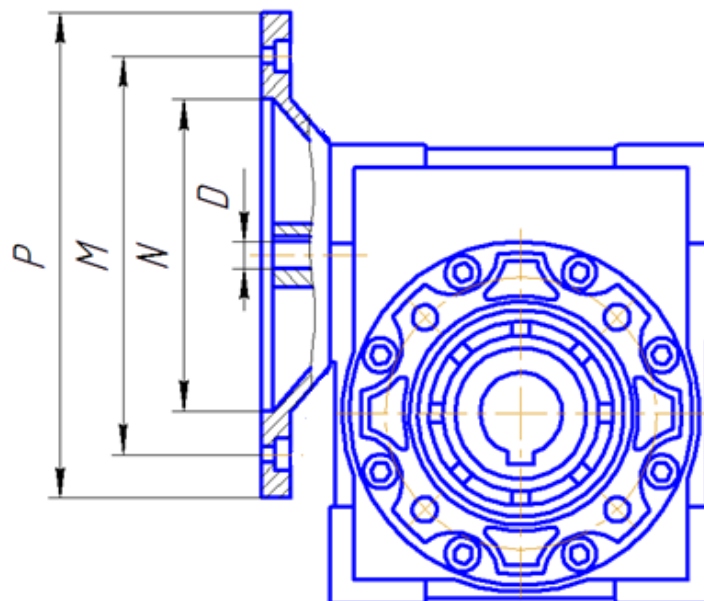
Червячный-редуктор NMRV-075-80-9-159 с обозначениями размеров присоединительного фланца и входного вала
